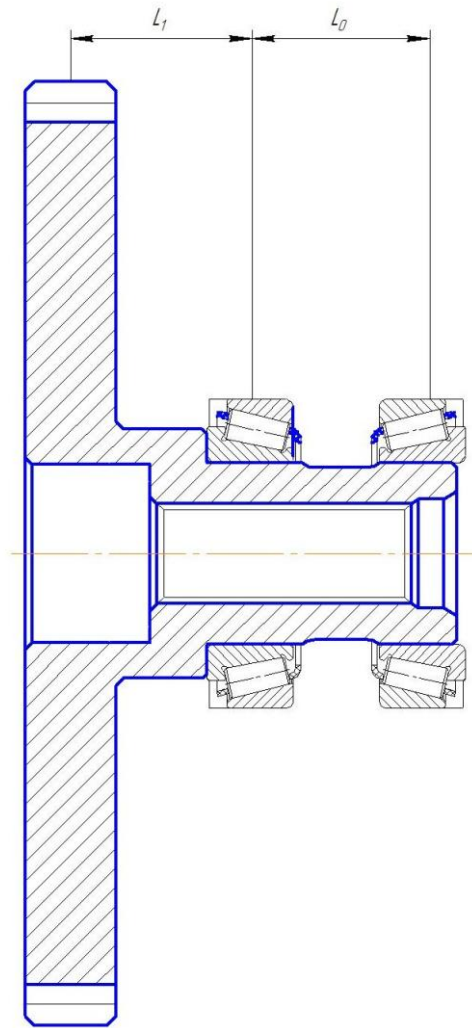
Компонка ведущего вала заднего колесного редуктора
